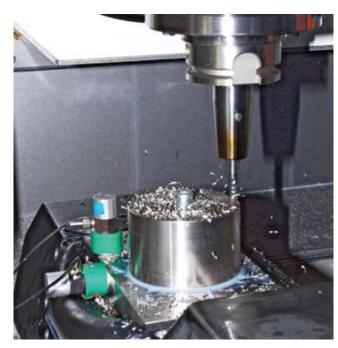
Обработка уступа фрезой, закрепленной в термопатроне
